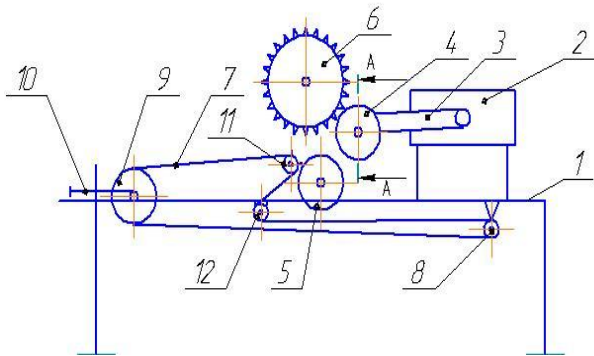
Схема и общий вид измельчителя: 1 – стойка; 2 – двигатель; 3 – механизм привода; 4 – основной вал с режущими ножами; 5 – подающий вал с протирежущими ножами; 6 – вал с циркуляционными дисками; 7 – транспортер; 8, 9 – ведущий и ведомый валы транспортера; 10, 11 и 12 механизмы натяжения 10, 11 и 12 транспортера
